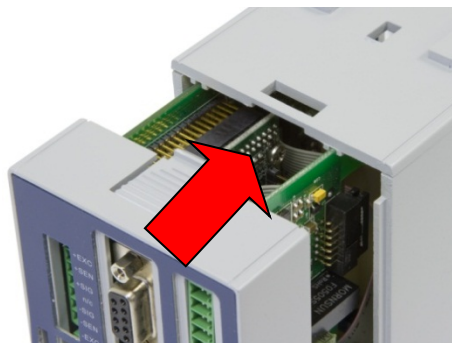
Inserción a presión de la tapa en su posición cerrada
